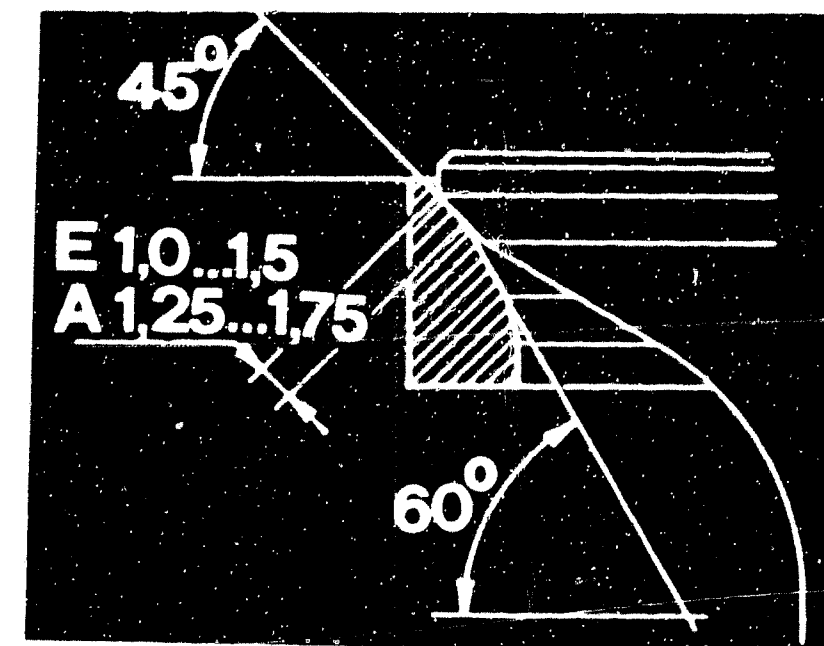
Bearbeitungswinkel und -masse der Ventilsitze. E = Einlassventil, A = Auslassventil.
